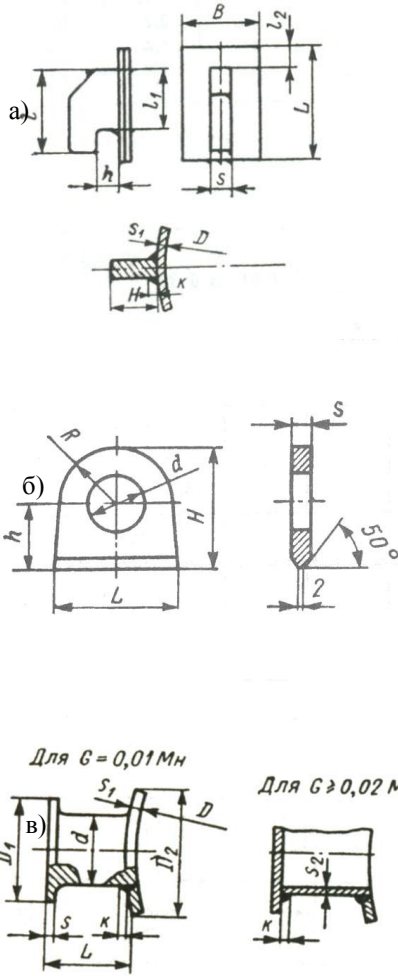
Строповые устройства аппаратов: а) крюк сварной; б) ушко приварное; в) цапфа приварная
